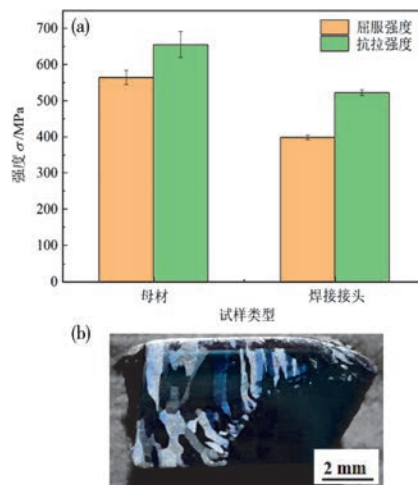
T-TIG-01-PWHT 焊接接头的 (a) 拉伸强度、屈服强度和 (b) 断口侧面组织
